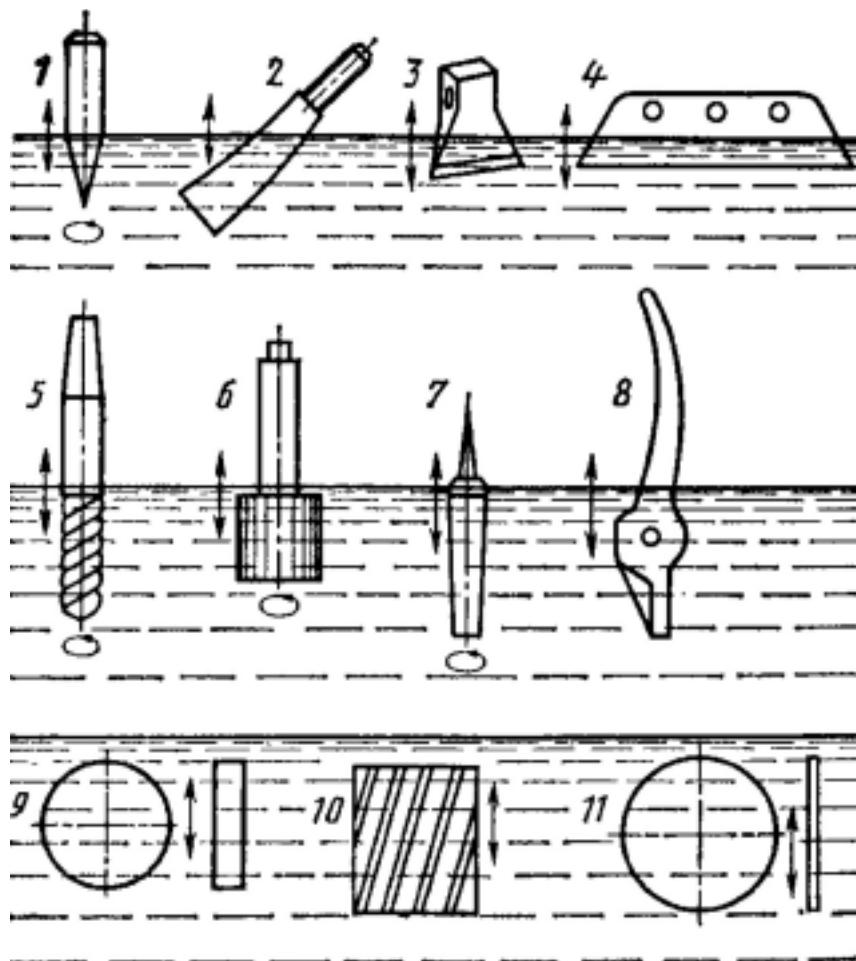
Способы погружения деталей в охлаждающую жидкость: 1 — зубило; 2 — зуб барабана молотилки; 3 — топор; 4 — лемех; 5 — сверло; 6, 9, 10 — фрезы; 7 — напильник; 8 — ручка плоскогубцев; 11 — дисковая пила
